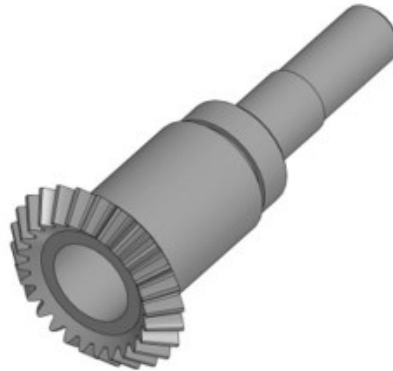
3D-модель деталі вал-шестерня 5154-18-22-А
